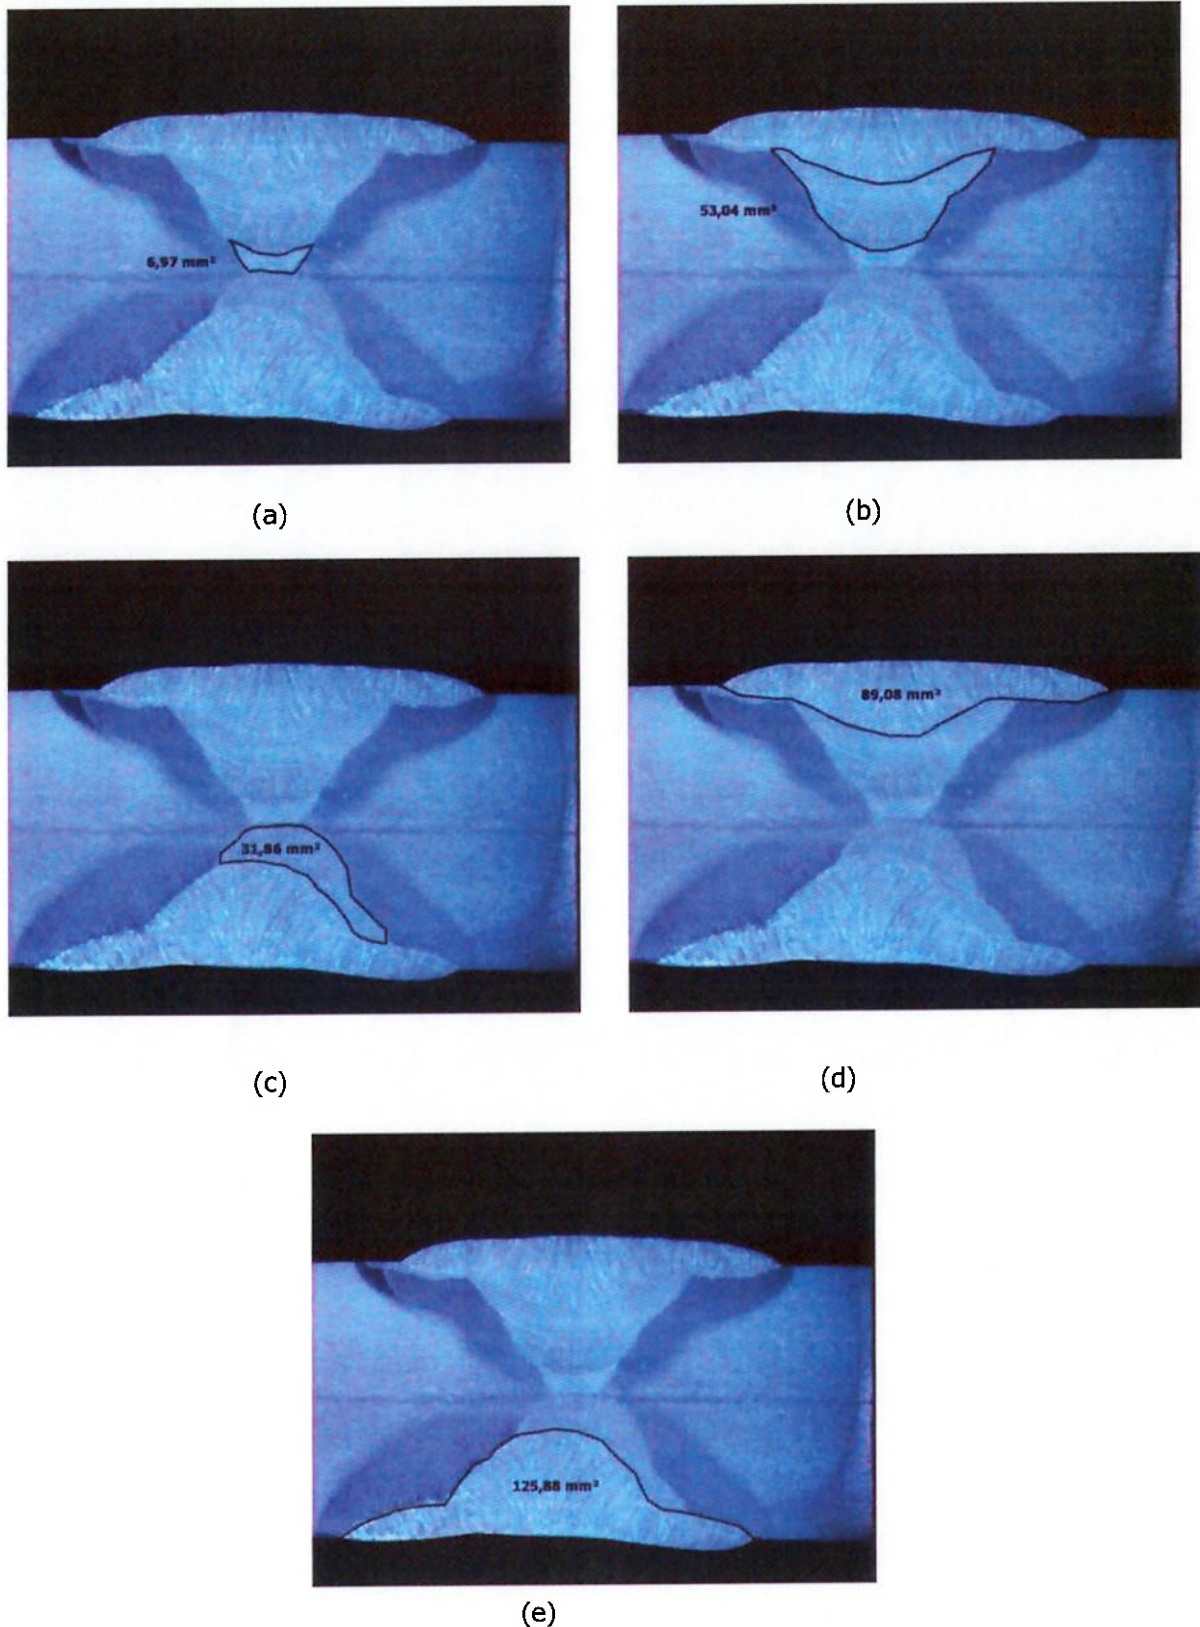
Junta soldada com 1 arame, seqüência de soldagem identificada pelo passe de raiz (a) passe seguinte de enchimento pelo lado da face (b) passe de enchimento pelo lado oposto da face (c) passe de acabamento pelo lado da face (d) passe de acabamento pelo lado oposto da face (e), ataque Nital 6%.
